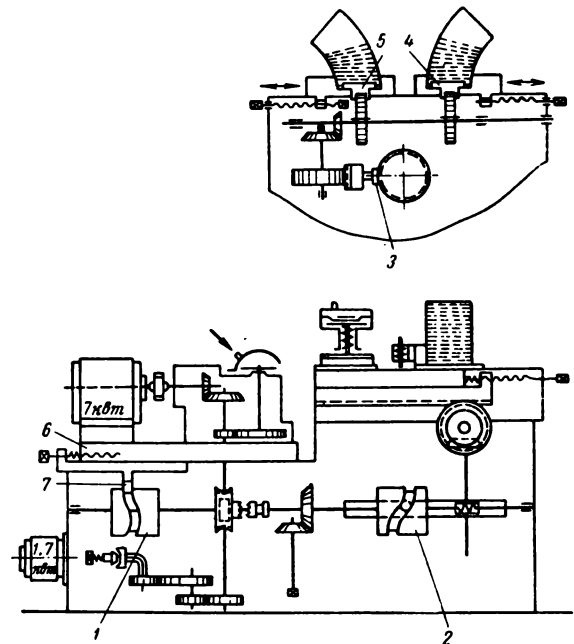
Схема автоматического фрезерного станка для коллекторных пластин.
